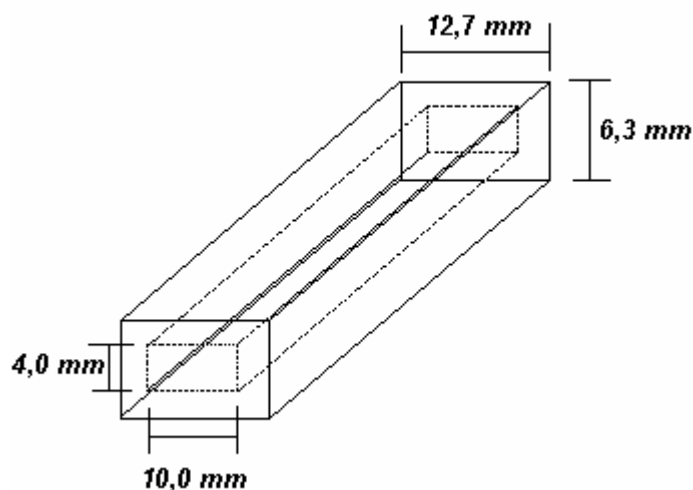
Esquema do corpo de prova usinado para retirar a camada superficial (skin).
